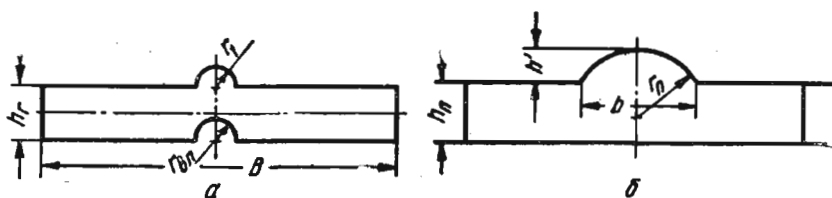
Профиль желобчатой рессоры (а) и ее предчистовой калибр (б)
